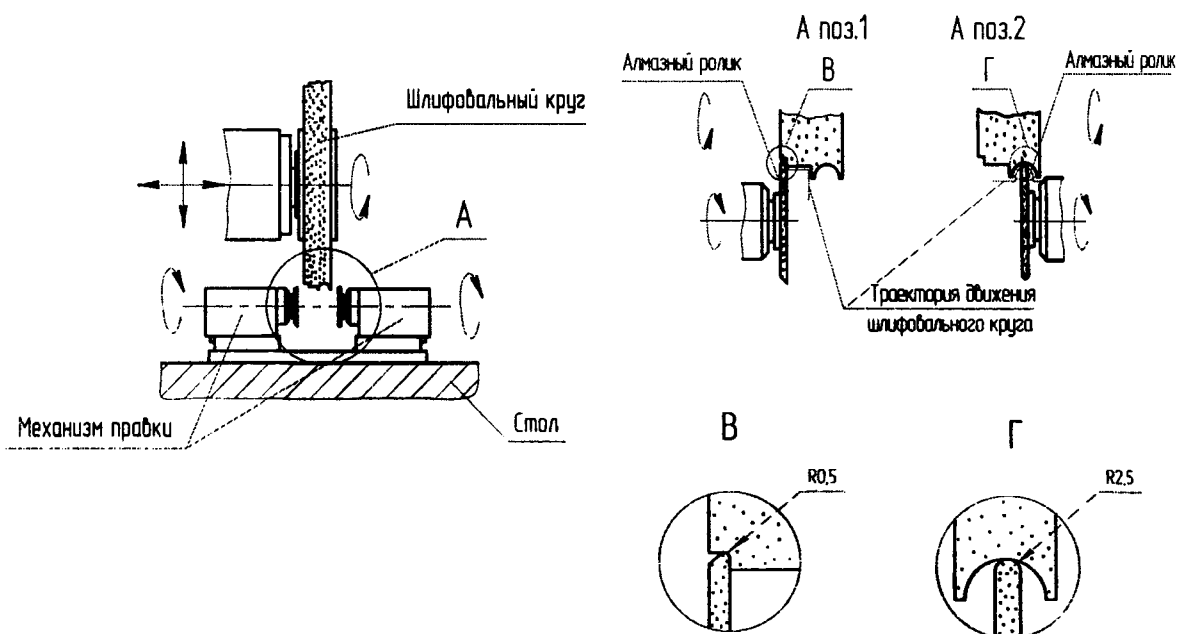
Правка шлифовального круга двумя алмазными роликами
